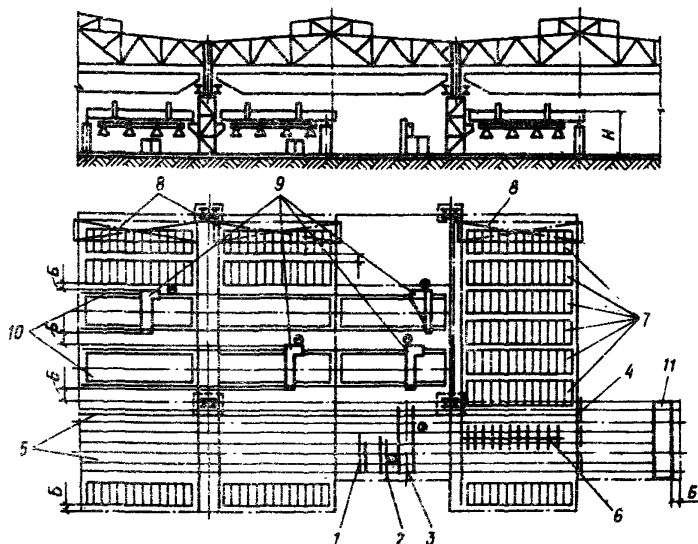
Размещение поточной линии стыковки и резки листового проката
